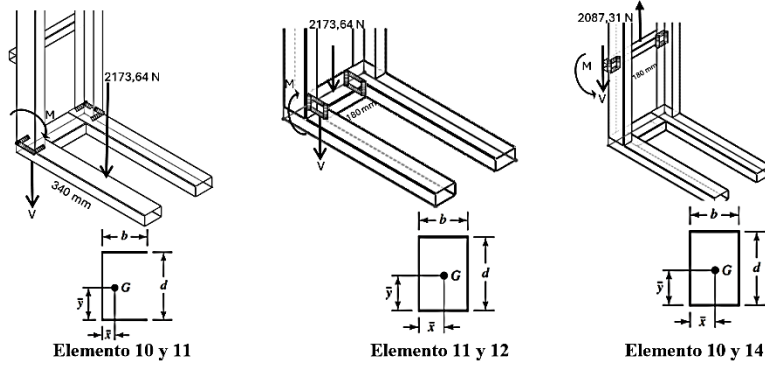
Análisis de soldadura en los elementos de la estructura del equipo.
